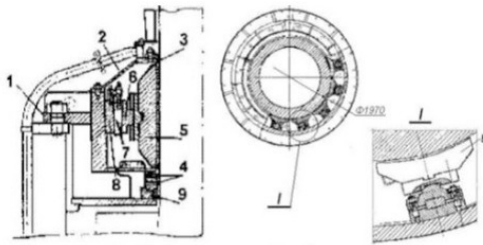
Направляющий подшипник гидротурбины (с самоустанавливающимися сегментами)
